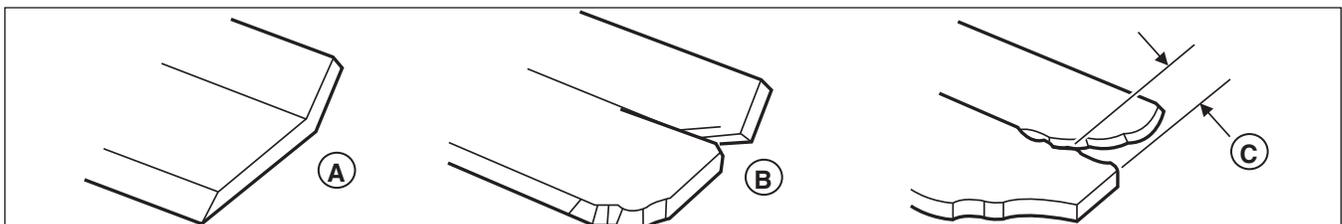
Inspección de los elevadores por aire de las cuchillas del cortacésped
